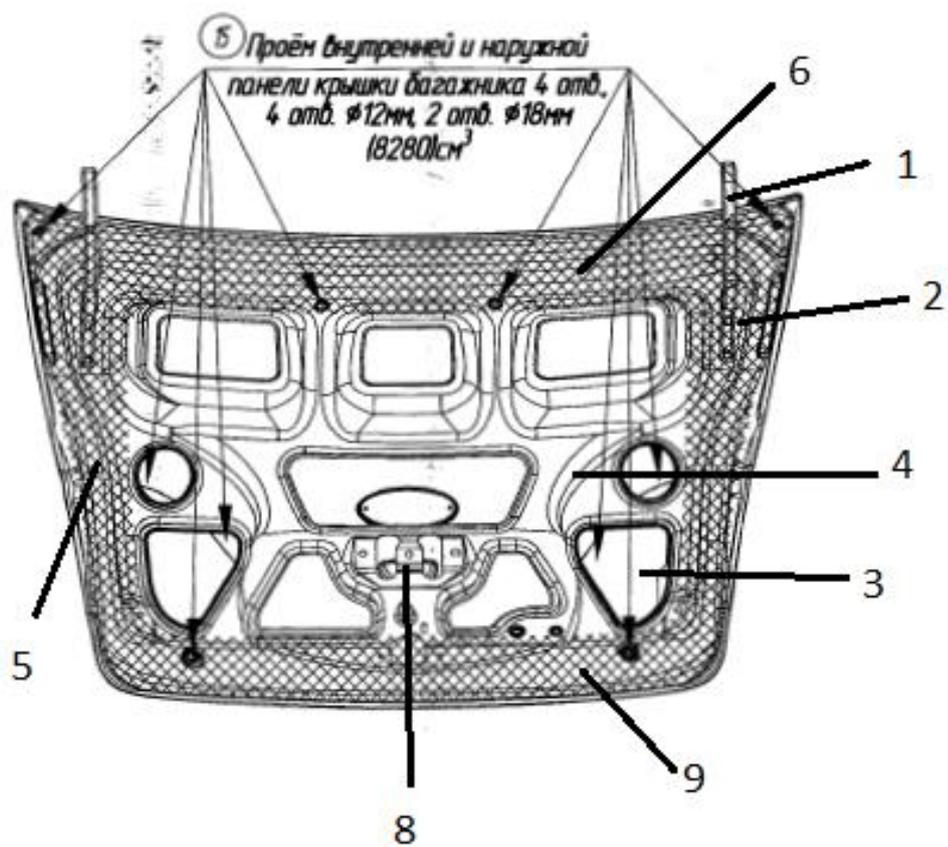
Поверхности установки оснастки крышка багажника в сборке
